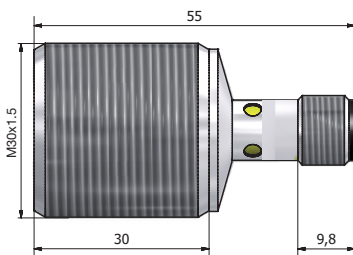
Kurze Ausführung, bündiger Einbau, Steckversion
